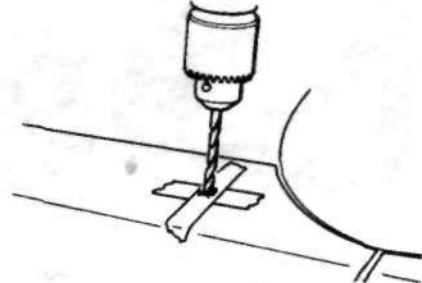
Сверление отверстия в кузове для установки антенны.
